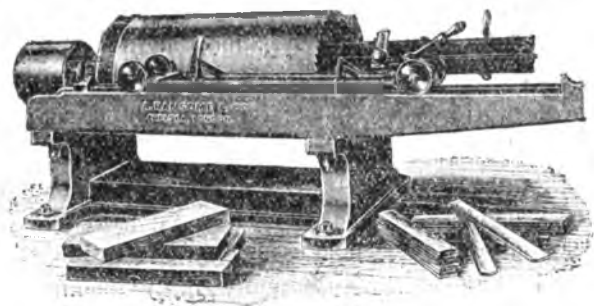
Станок с цилиндрической пилой для выпиловки клепок.
